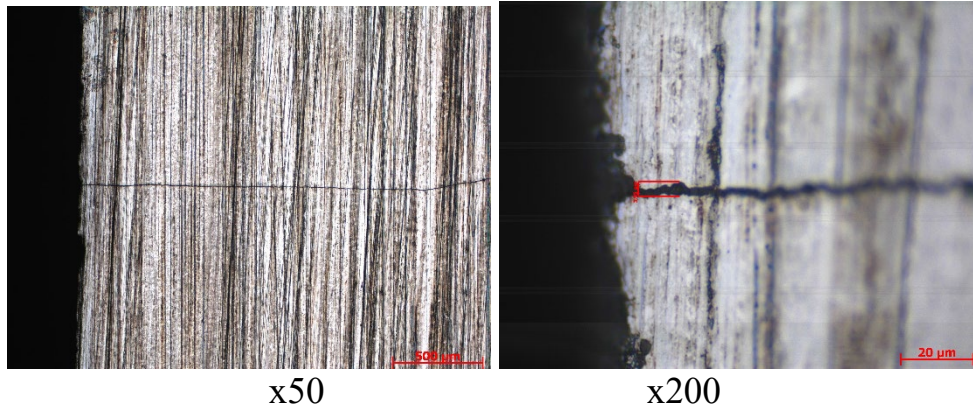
Загальний вид передніх поверхонь твердого сплаву марки ВК8 після заточування колами з карбіду кремнію
